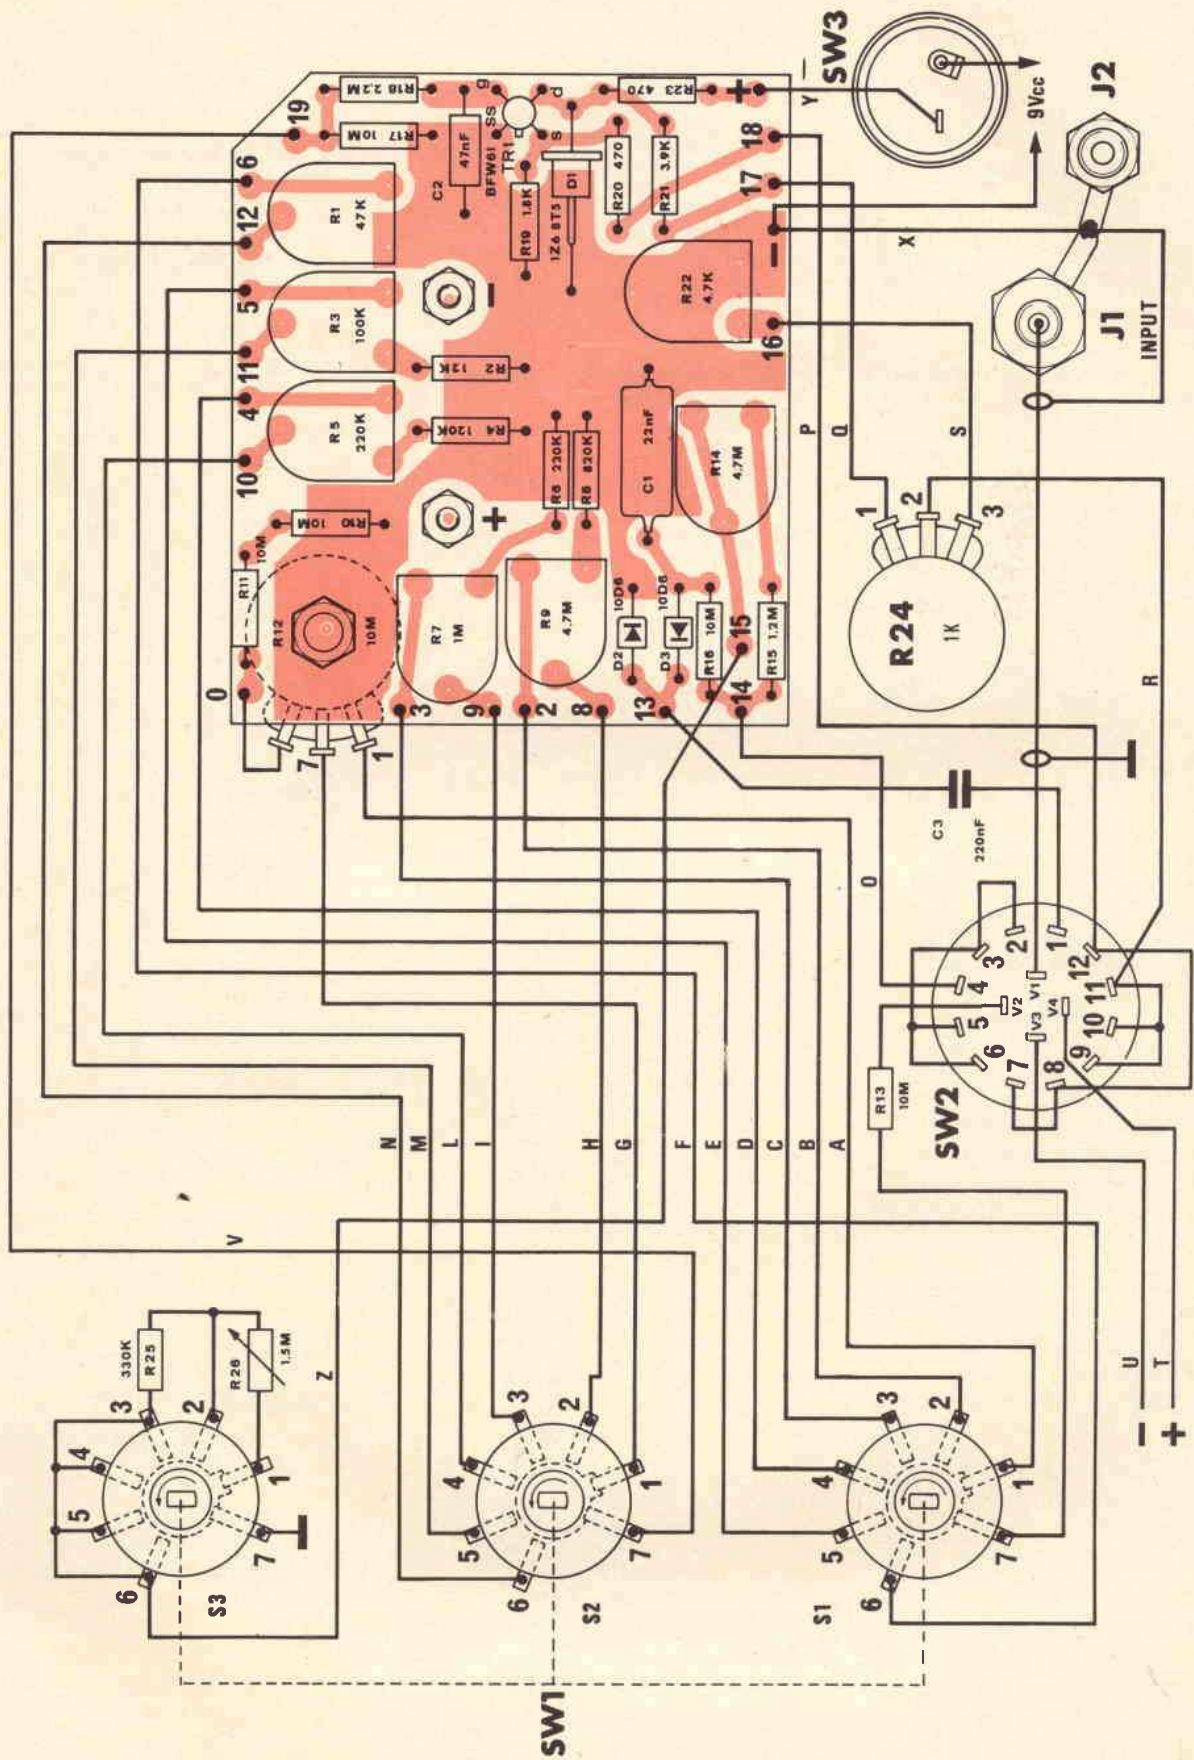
Cablaggio fra circuito stampato e componenti esterni.
